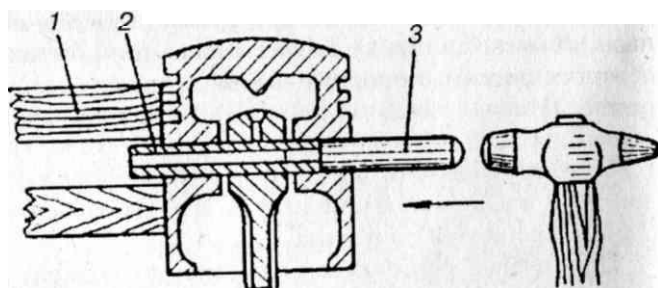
Выпрессовка поршневого пальца при помощи молотка: 1 - деревянный брус; 2 - поршневой палец; 3 - выколотка
